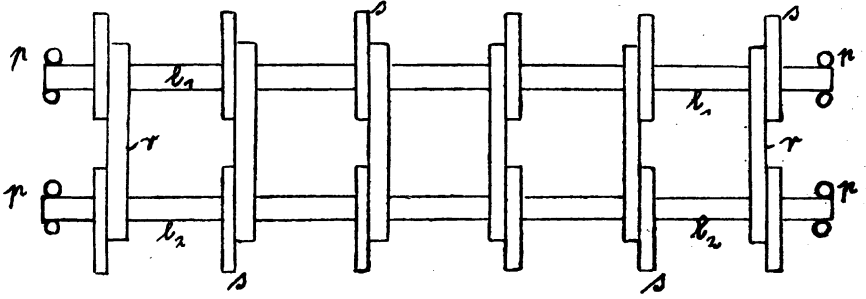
Aufsicht auf die Senfmaschinenbank.
